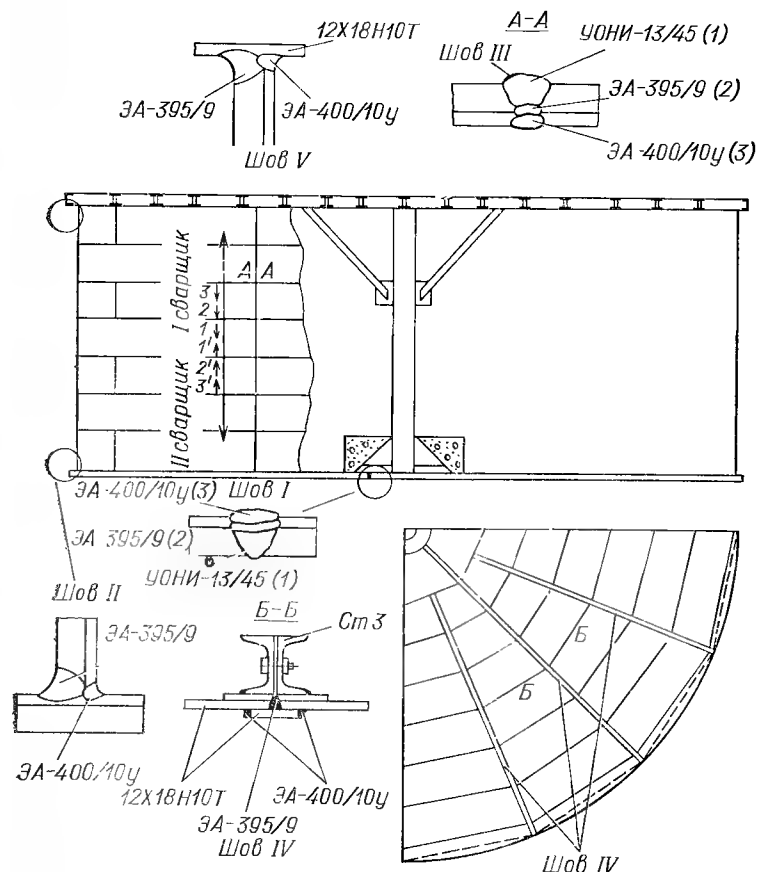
Схема сварки резервуара для хранения конденсата на АЭС.
